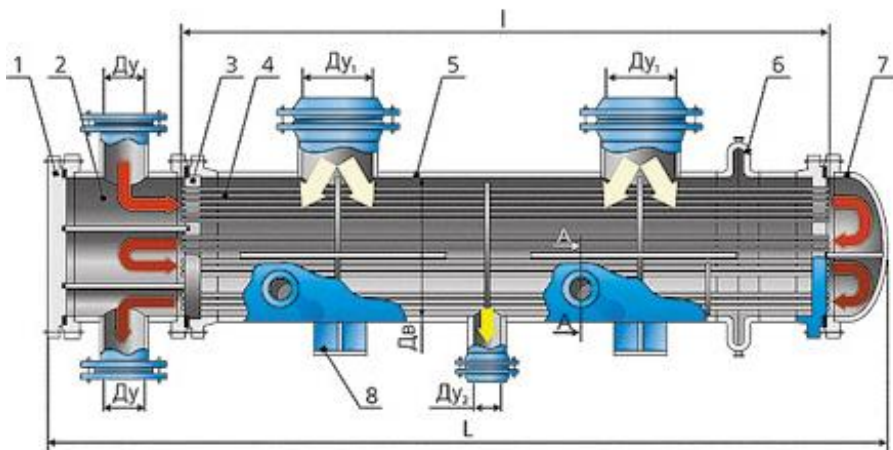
Горизонтальний фреоновий кожухотрубний конденсатор: 1 – кришка розподільчої камери; 2 – розподільча камера; 3 – решітка трубна; 4 – труба теплообмінна; 5 – кожух; 6 – компенсатор; 7 – кришка кожуха; 8 – опора
